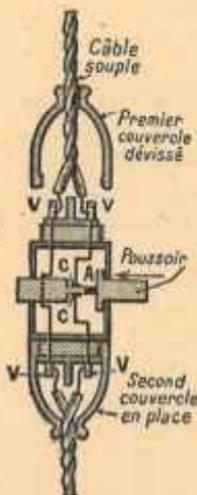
Interrupteur à poussoir sur câbles souples.
